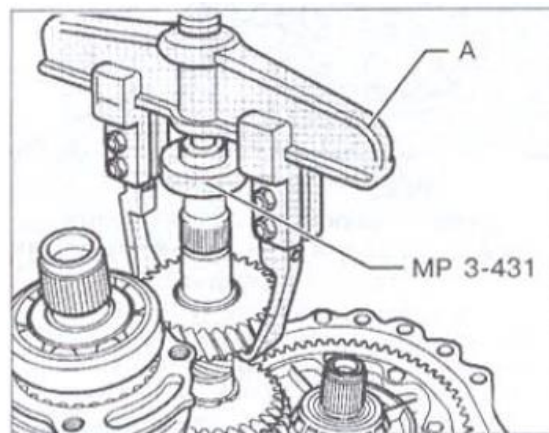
Схема знімання шестерні четвертої передачі
